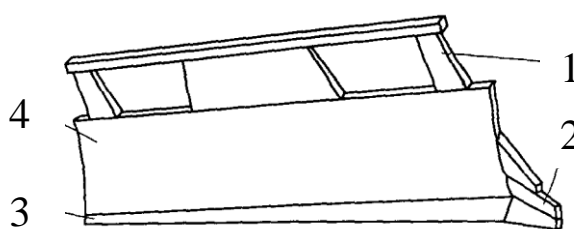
Однокорпусной косо поставленный кусторезный отвал:
